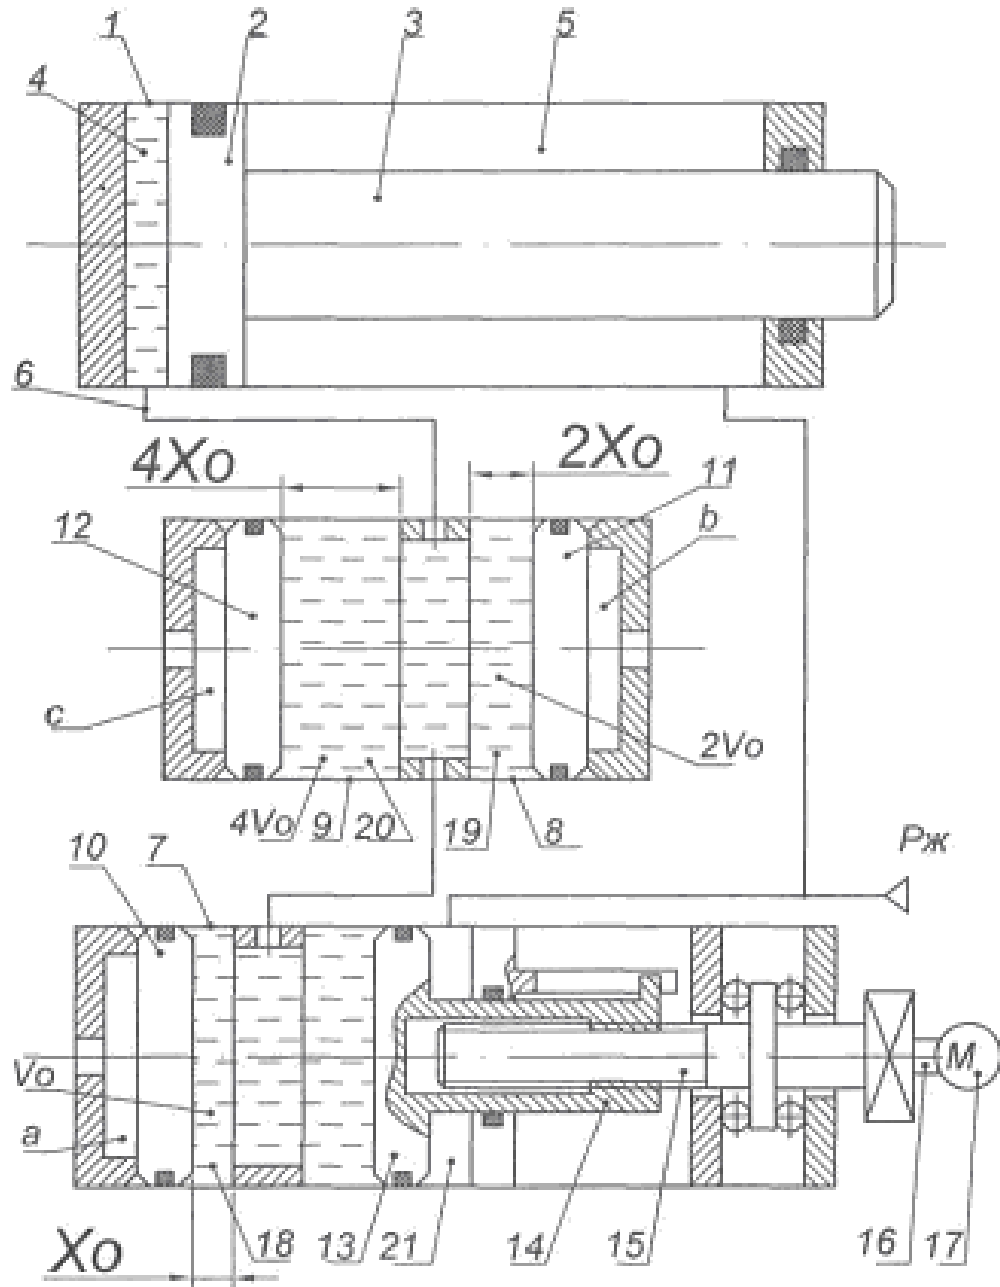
Багатопозиційний пневмоелектричний привод.
